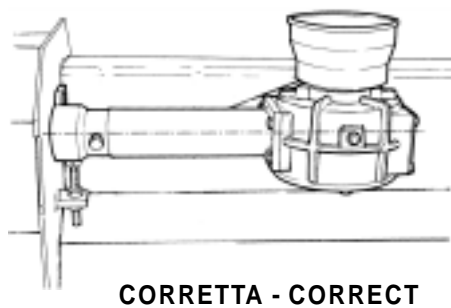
Posizione scatola ingranaggi - Gearbox position
